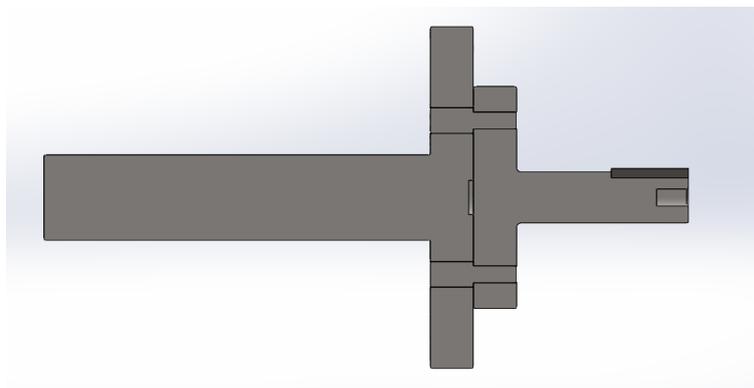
Corte por sección de vista de alzado del conjunto fusible mecánico.
